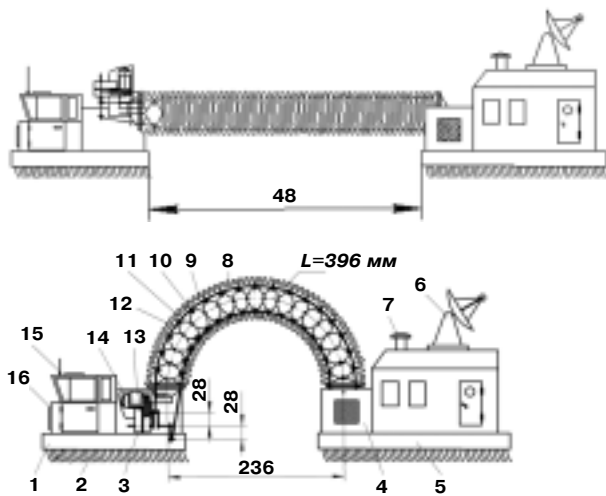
Общий вид и конструкция шагополза: 1, 5 — платформы щеток; 2 — направление ворса; 3 — редуктор; 4 — аккумуляторный отсек; 6 — локатор; 7 — труба; 8 — суровая нить; 9 — проставочные втулки; 10 — ролики; 11 — гофрированный шланг; 12 — ромбический элемент цепи; 13 — электродвигатель; 14 — контакты электромотора; 15 — антенна; 16 — кабина.
